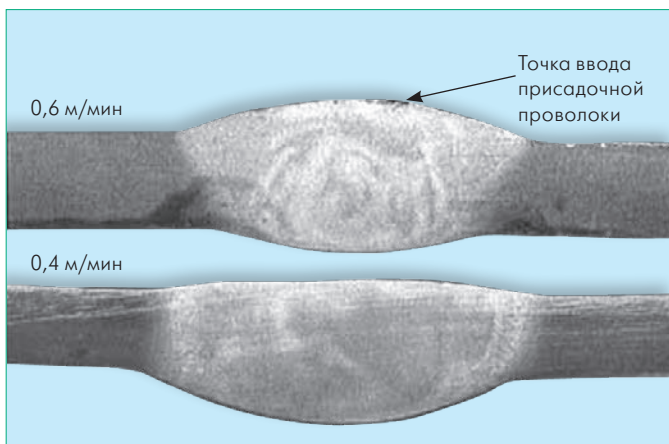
Поперечное сечение сварки стыком для образца 2014 толщиной 1,6 мм с использованием присадочной проволоки типа 5356 при скорости перемещения 0,6 и 0,4 м/мин
